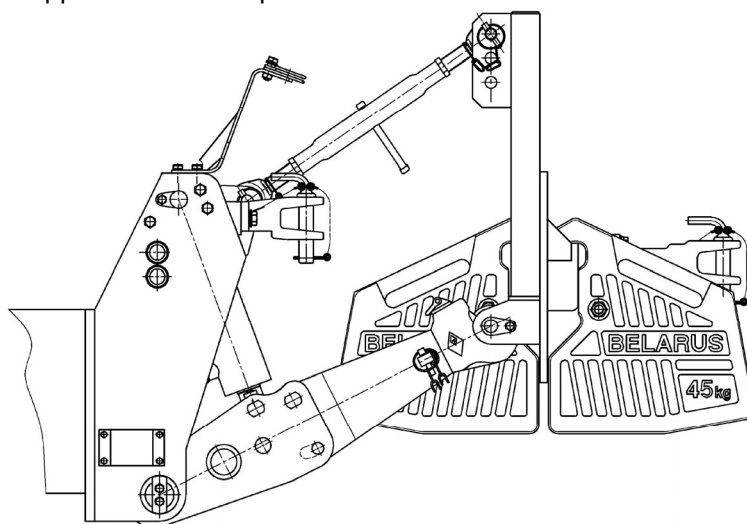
Схема установки навесных балластных грузов на ПНУ
